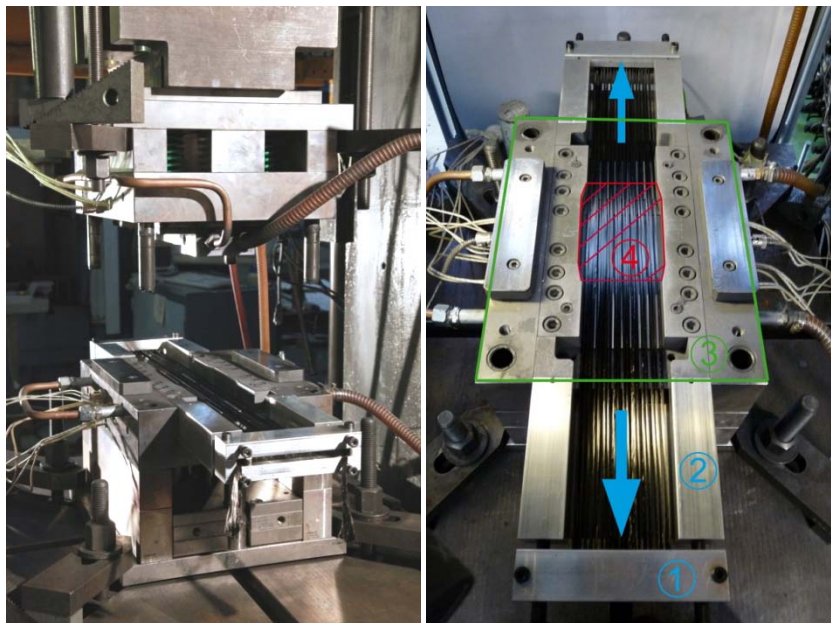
Vorspannvorrichtung im eingebauten Zustand; *links*: vollständige Darstellung des Werkzeugs; *rechts*: Draufsicht des unteren Teils des Werkzeugs mit Beschriftung ((1) Vorspanneinrichtung, (2) Abstandhalter, (3) Kontur des Werkzeugs, (4) Kontur des Aluminiumanteils nach dem Umformen)
